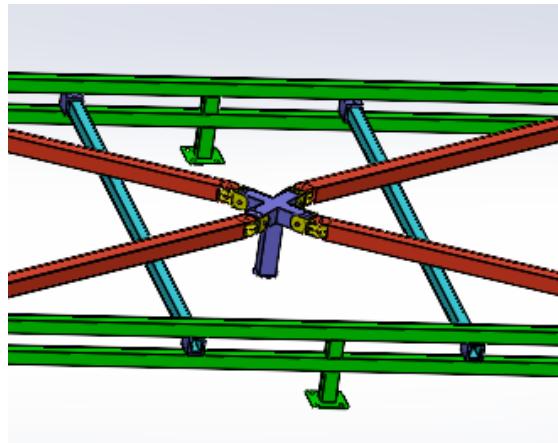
Fixation des barres de support transversales aux barres longitudinales
